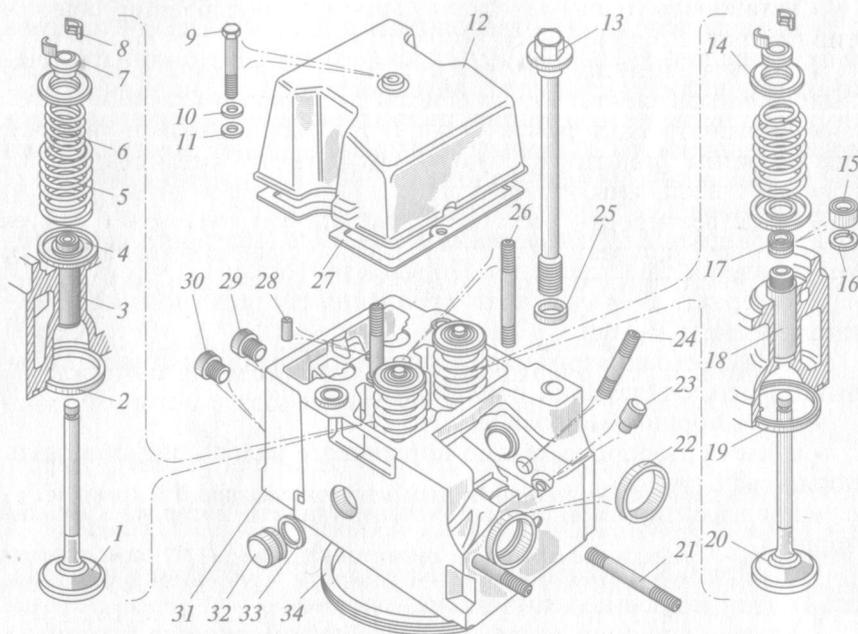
Разобранная головка цилиндра с клапанами:
